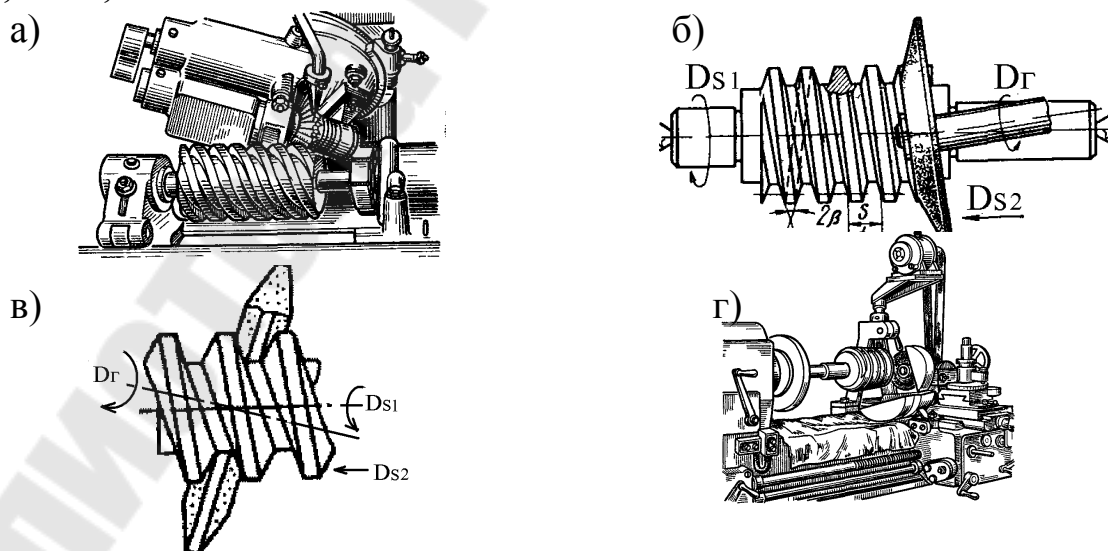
Обработка червяков: дисковой фрезой (а); шлифовальным кругом (б, в) и устройство для шлифования червяка на токарном станке (г)
